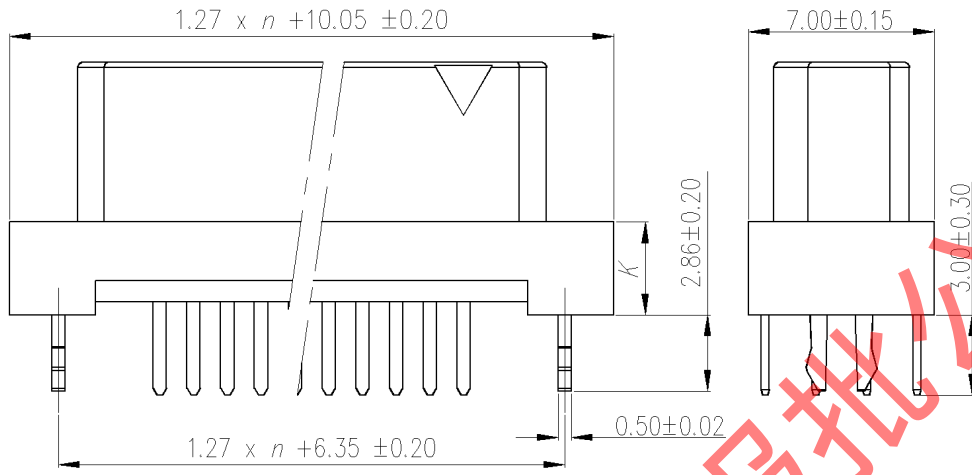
H类型插座 90度穿孔焊接式外形尺寸
